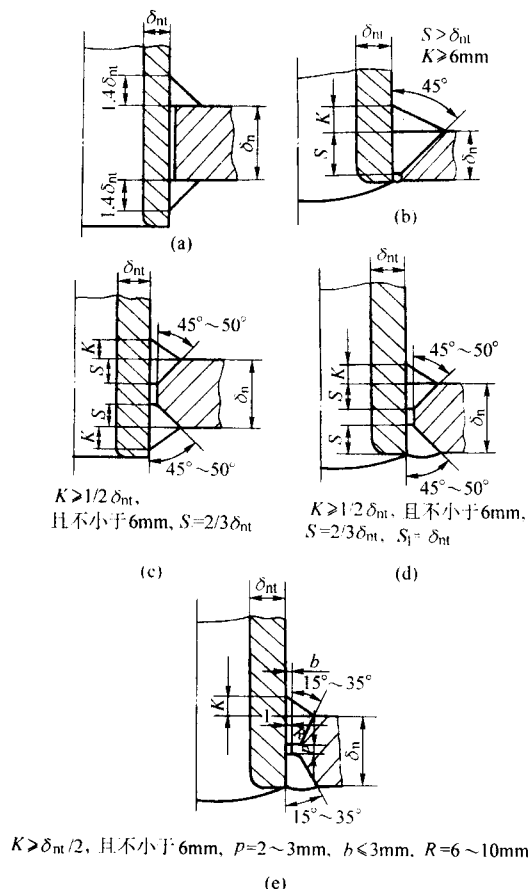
接管与壳体连接的局部焊透的焊接接头
